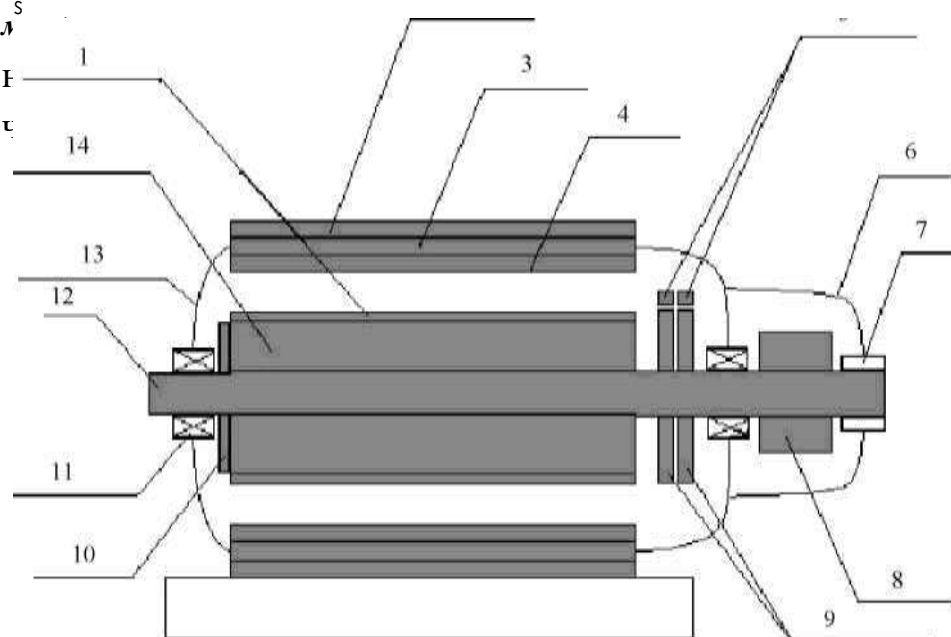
Конструктивная схема синхронной машины: 1 — обмотка возбуждения ротора; 2 — станина; 3 — сердечник статора; 4 — обмотка статора; 5 — щеточный аппарат; 6 — кожух; 7 — втулка; 8 — возбудитель; 9 — контактные кольца; 10 — крыльчатка вентилятора; 11 — подшипники; 12 — вал; 13 — вал ротора; 14 — вал статора.
